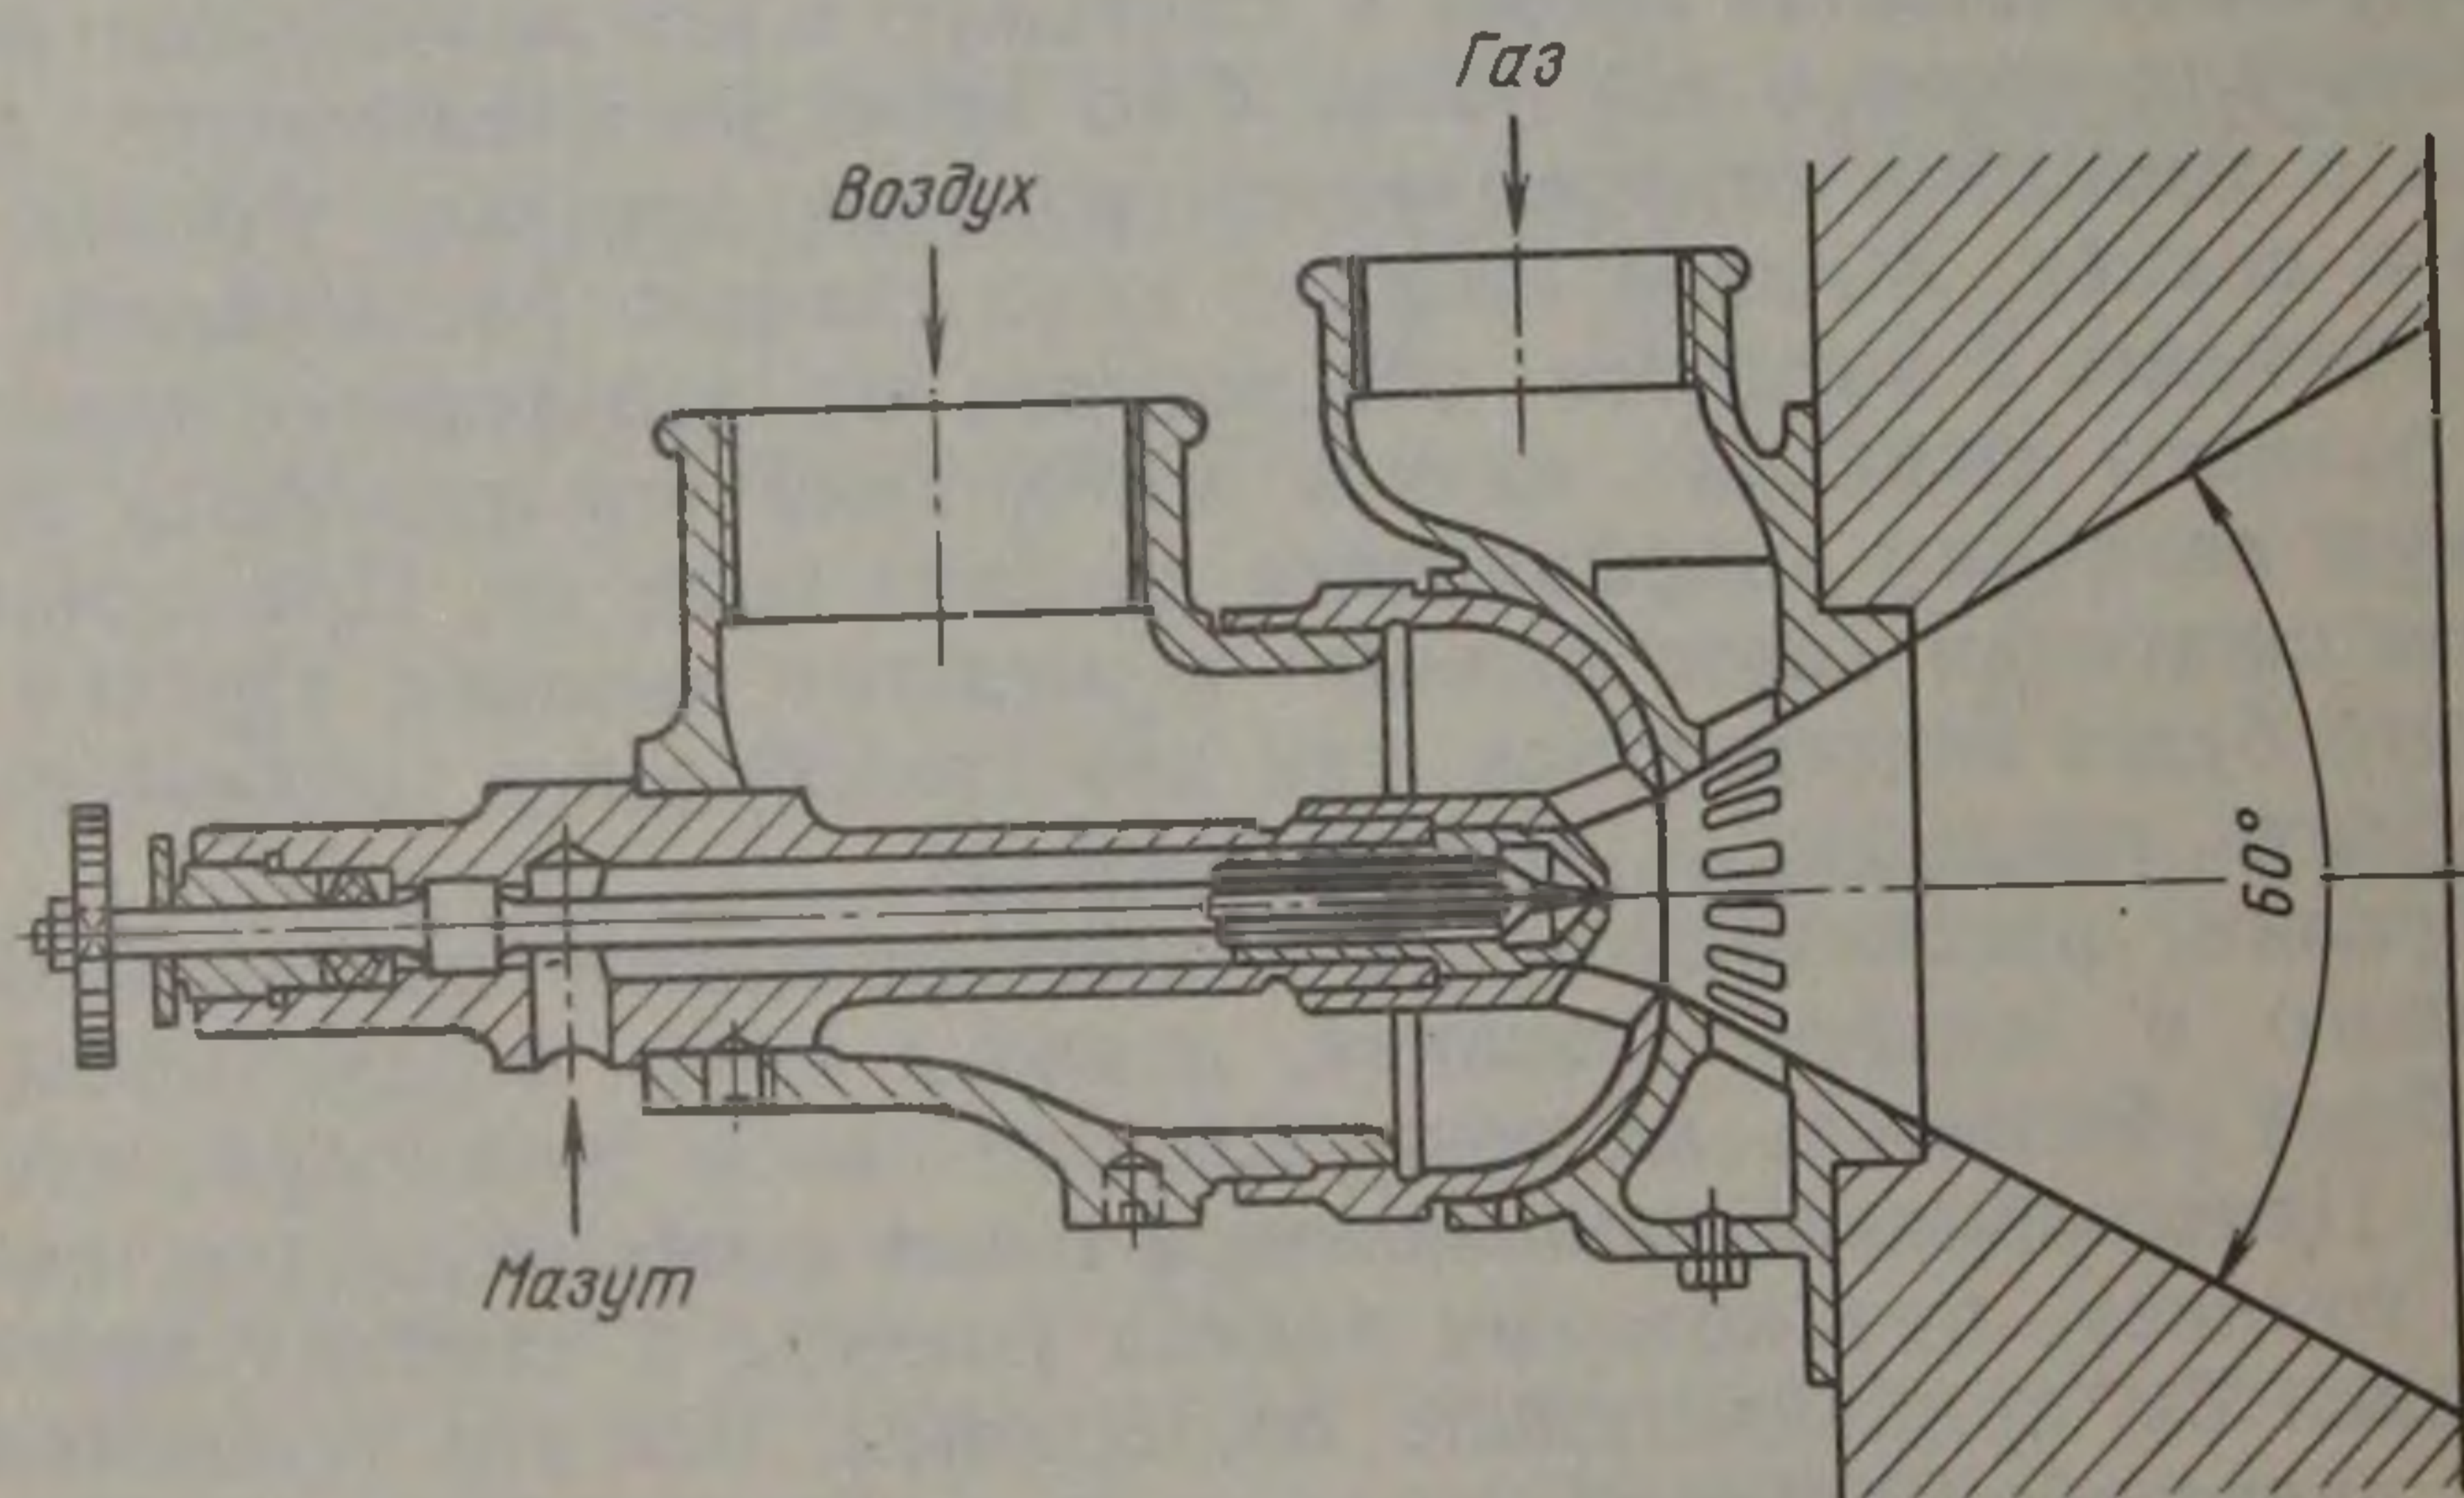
Форсунка А. И. Карабина, приспособленная для газо-мазутного отопления
